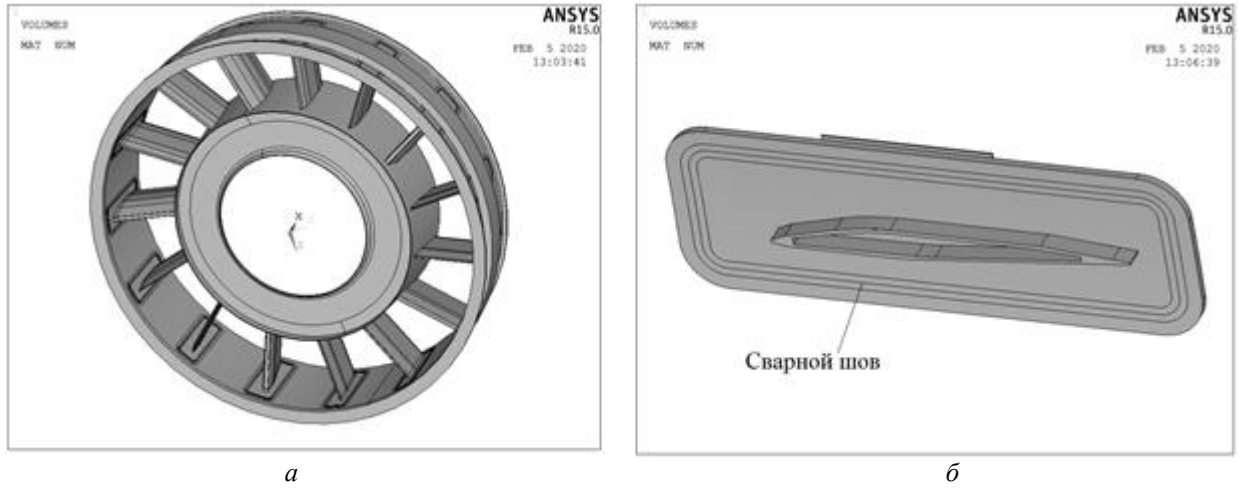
Общий вид геометрии узла авиационного двигателя (а) и фрагмент геометрии со сварным швом (б)
